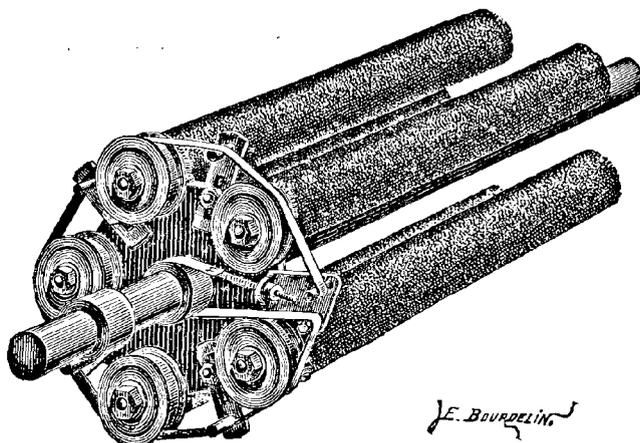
Tambour laineur de la machine Gosselin; extrémité portant la courroie-frein.
